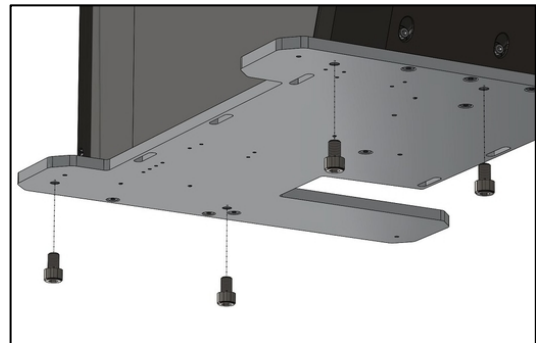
Montieren Sie die Maschine auf einem Ständer oder Gestell mit einem 6mm-Inbusschlüssel.
